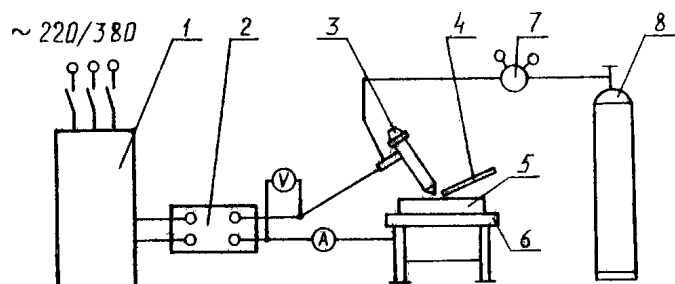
Схема установки для сварки алюминия в среде аргона:
